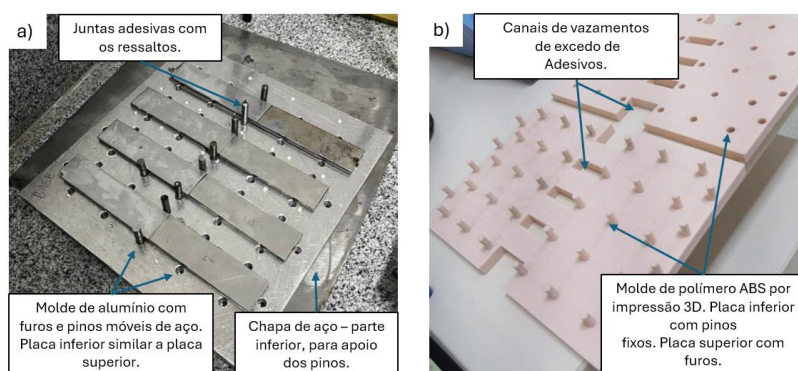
Moldes para juntas adesivas. a) Molde de alumínio com pinos de aço e chapa de sustentação de aço inoxidável e b) Molde de ABS por impressão 3D com pinos fixos.
